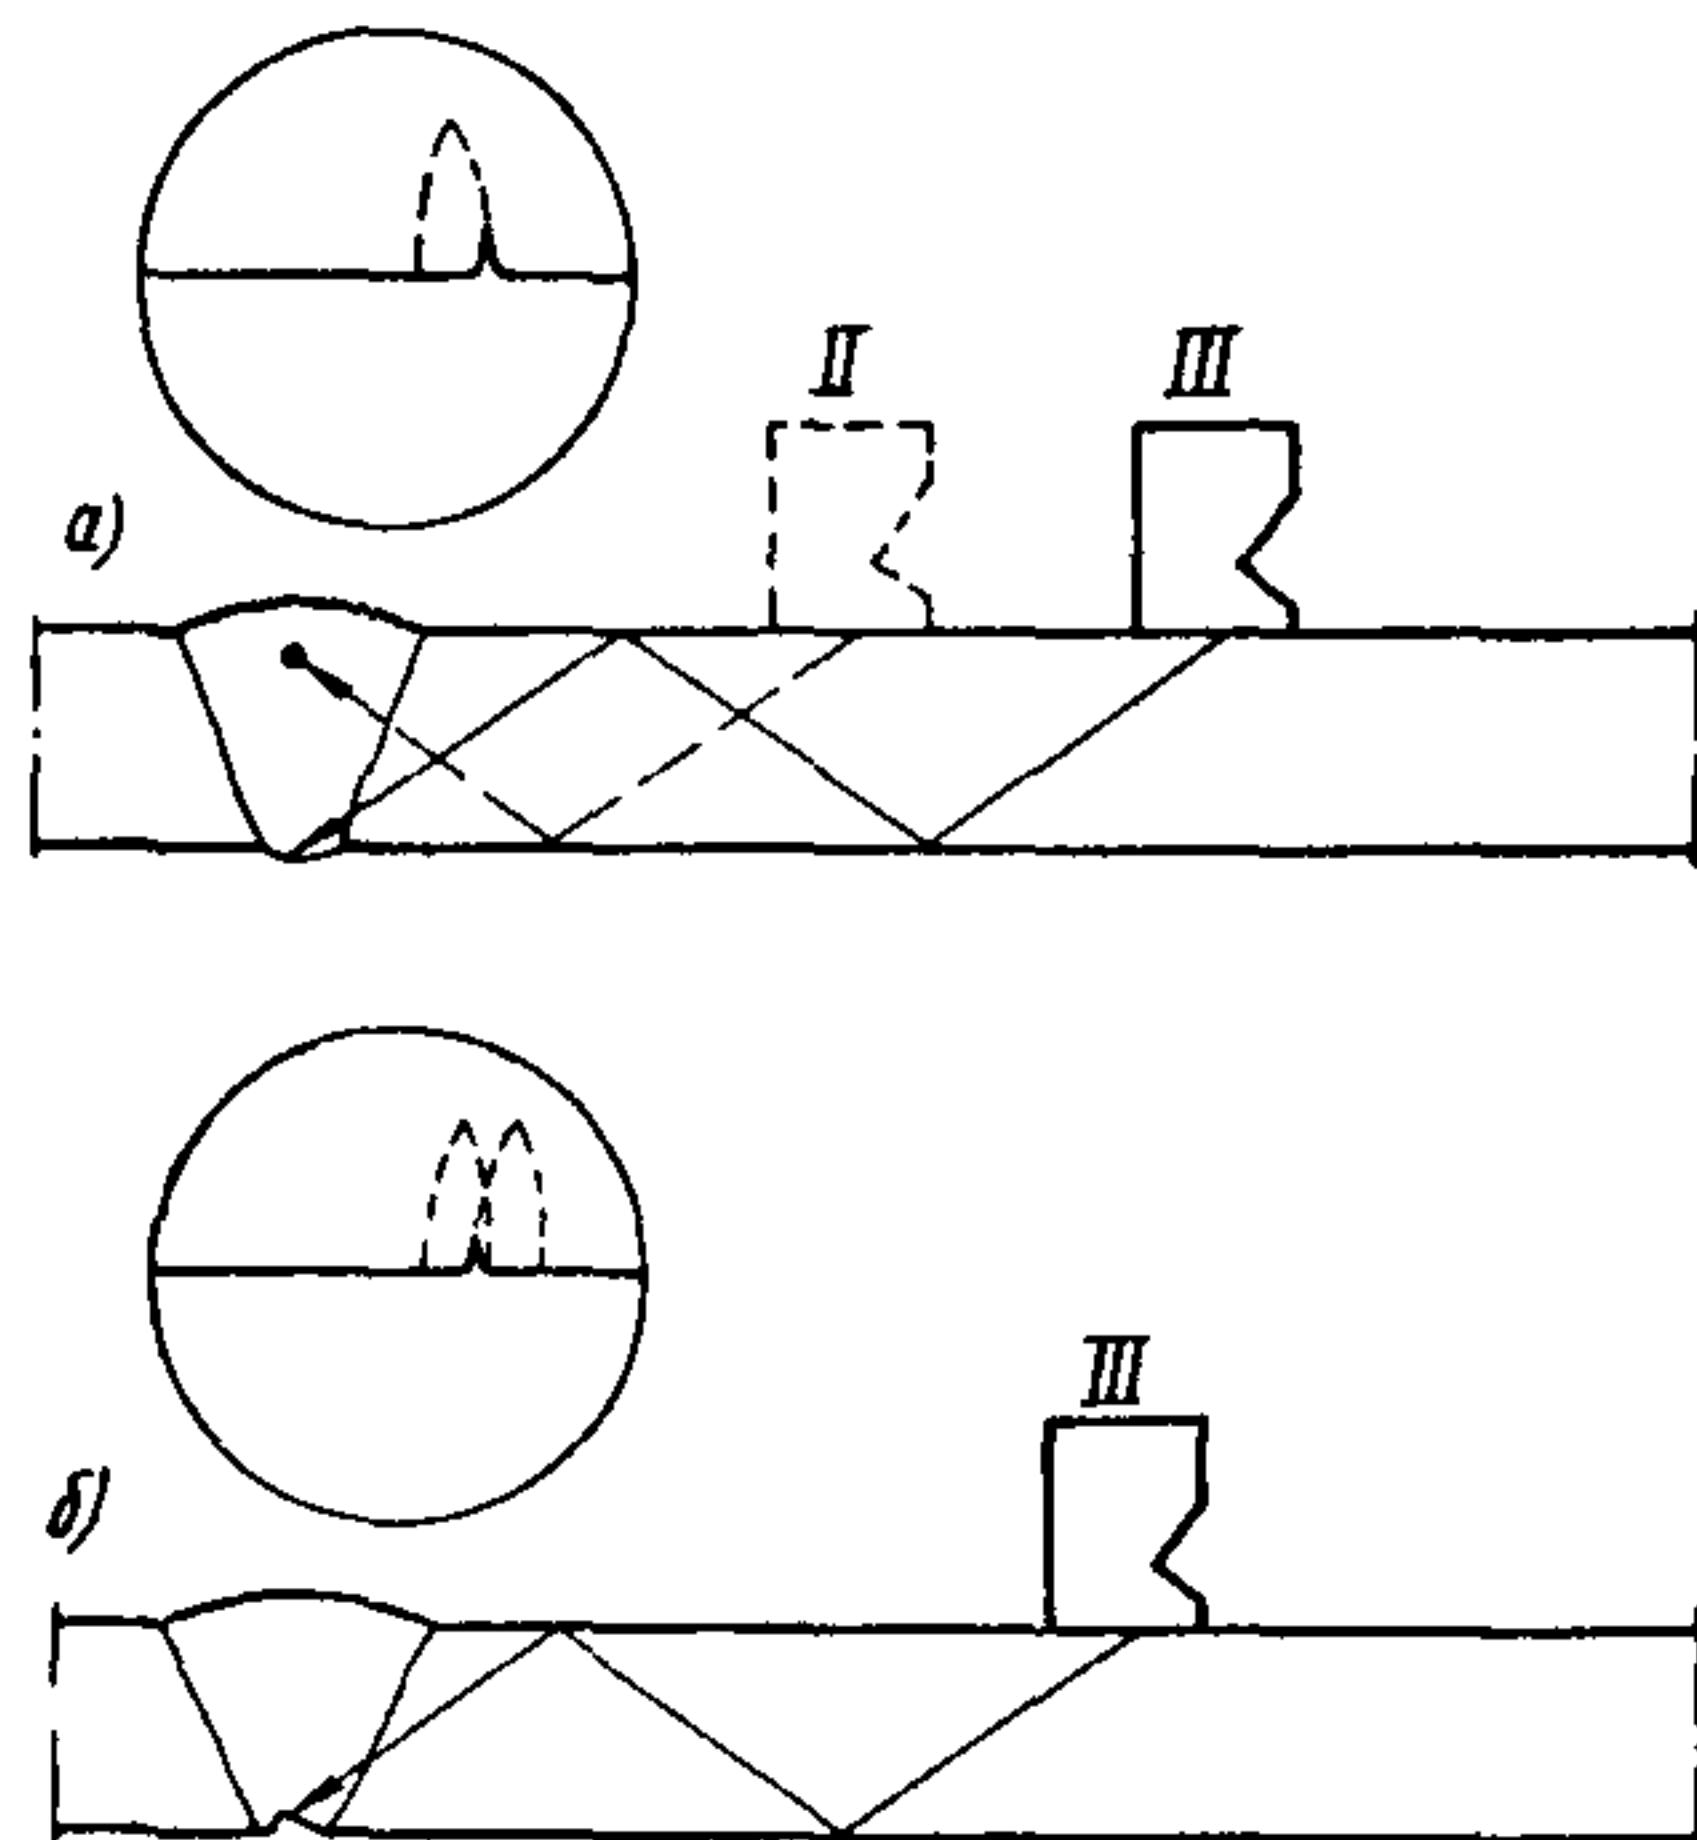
Контроль сварного стыка, сваренного на удаляемом подкладном кольце
